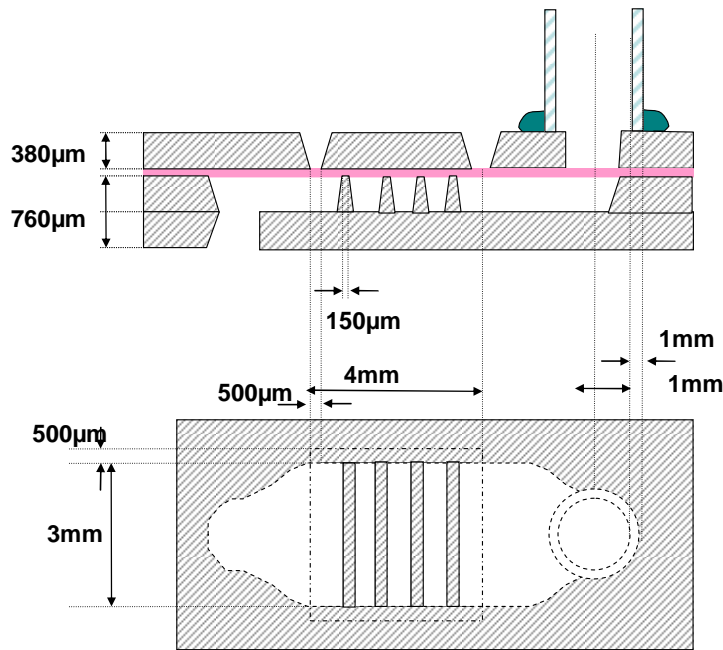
9. Géométrie et dimensions de la microvalve à membrane souple.
